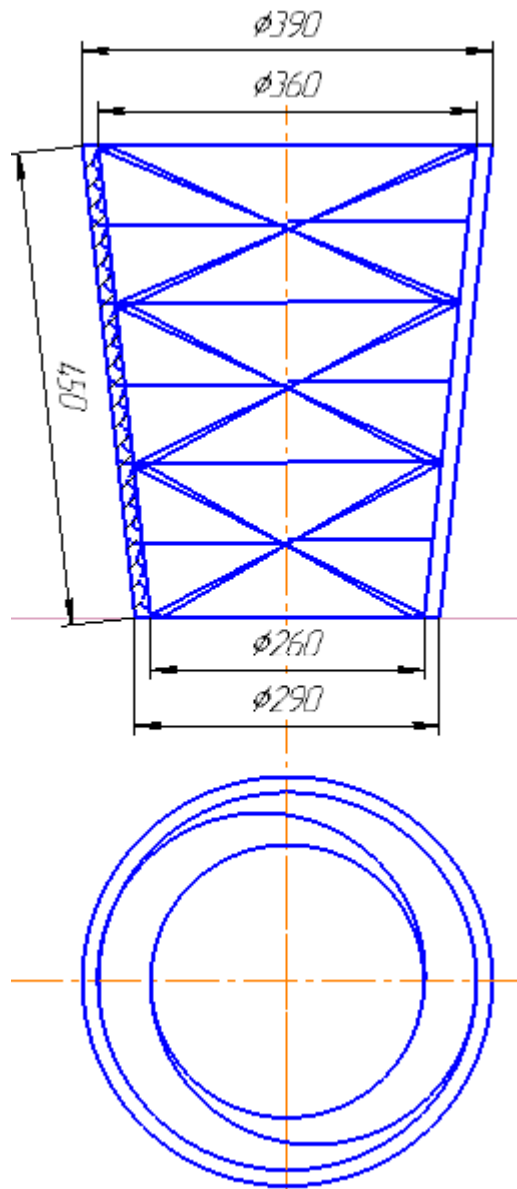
Зовнішній вид робочої камери (3);
